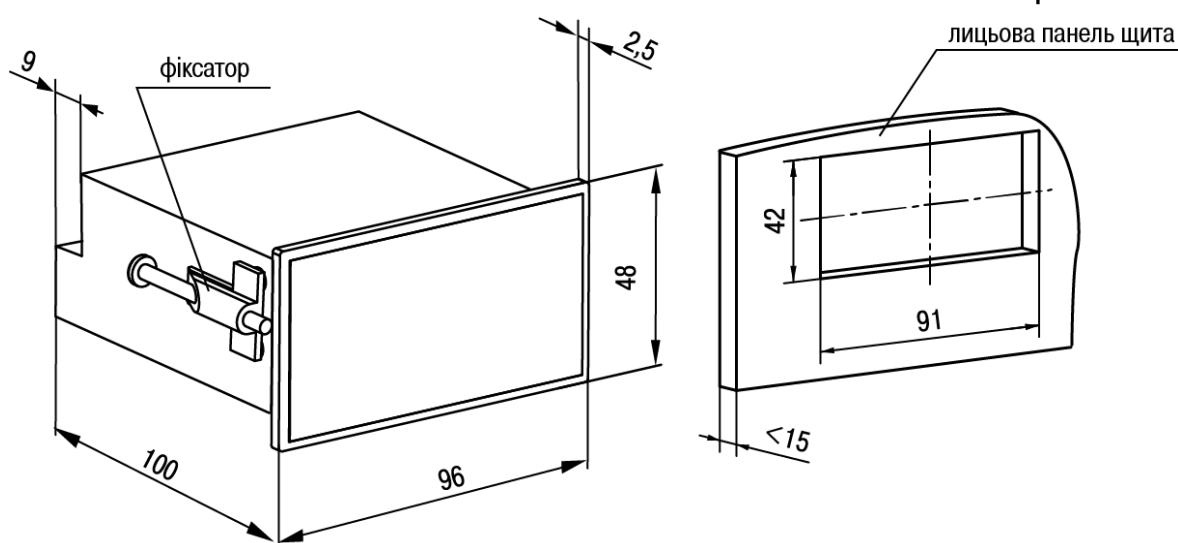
Габаритні розміри корпусу Щ2
